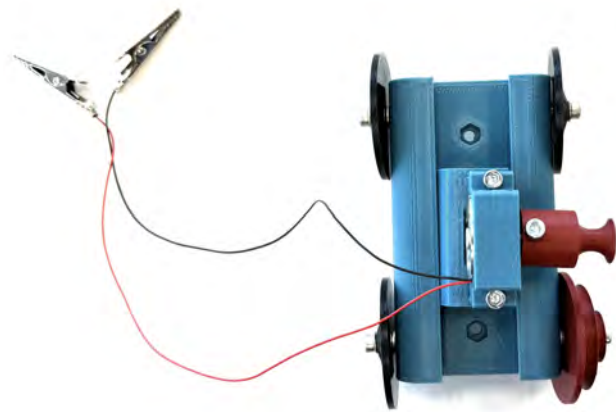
Der Motoraufsatz wird vorsichtig auf der Motorwelle verschraubt.
